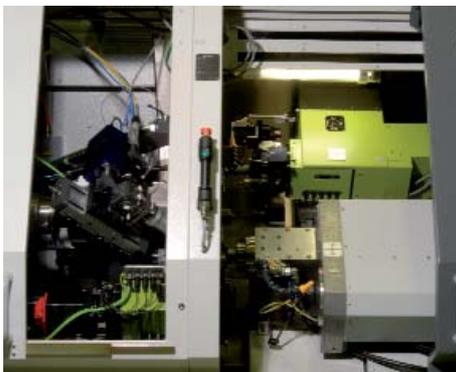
Drehmaschine des Herstellers Benzinger mit integrierter Laseroptik im Antriebsraum (links)
